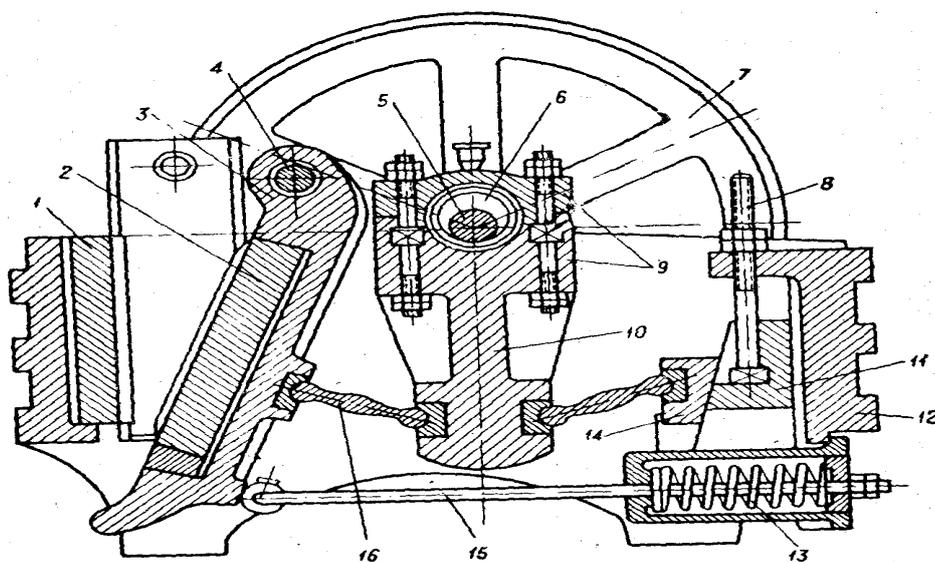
Щековая дробилка с простым движением щеки: 1 – неподвижная щека; 2 – съемная плита; 3 – подвижная щека; 4 – ось; 5 – вал; 6 – эксцентрик; 7 – маховое колесо; 8 – винт; 9 – подшипники; 10 – шатун; 11 – подвижный ползун; 12 – станина; 13 – пружина; 14 – ползун; 15 – тяга; 16 – распорная плита
